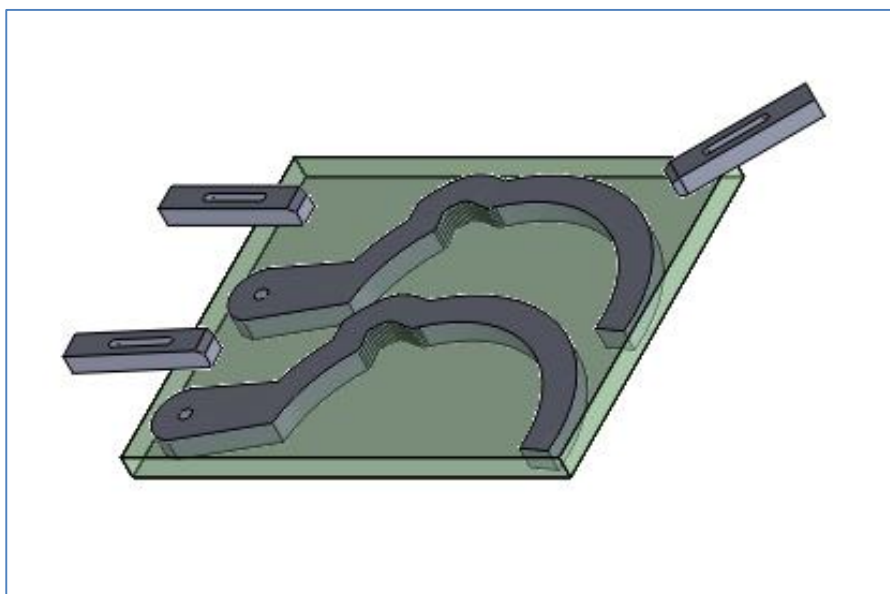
Ensamble de levas, blank y checks en SolidWorks
